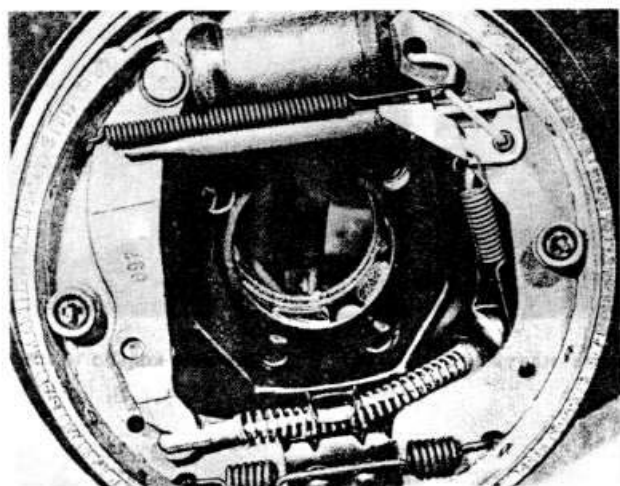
Правильная сборка деталей заднего тормозного барабана. Ступица снята.
